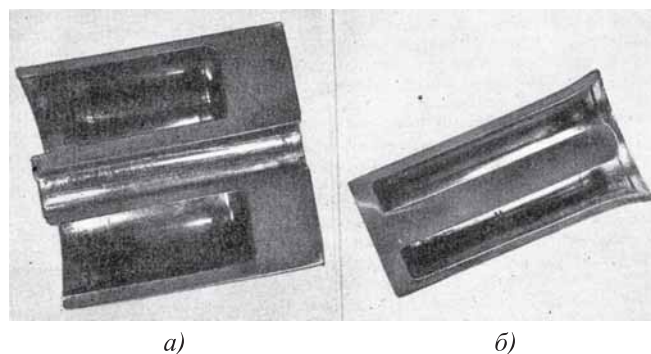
Фрезерованные по меридиональной поверхности образцы изготовленных холодным двухканальным выдавливанием экспериментальных деталей из различных сталей: а — сталь 10; б — сталь 15X
